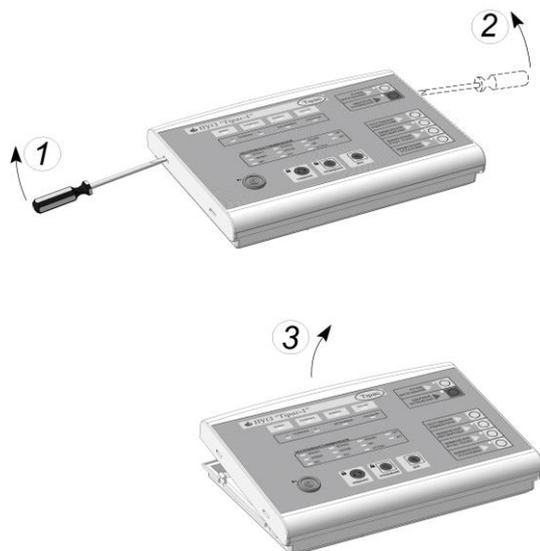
Порядок открывания корпуса ПУиЗ
